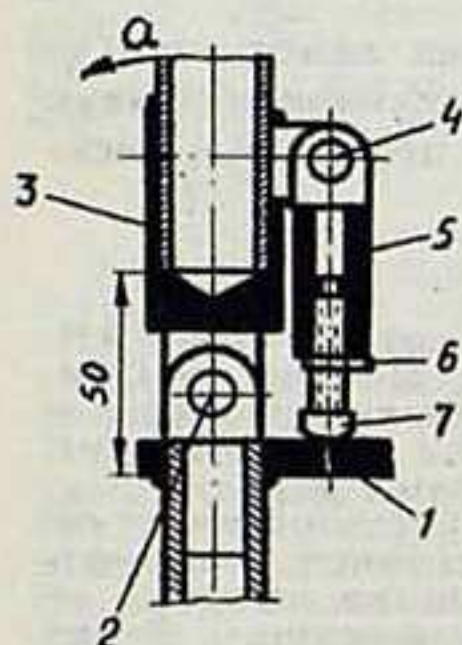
Механизм поворота спинки: 1 — основание; 2 — ось поворота; 3 — кронштейн; 4 — ось поворота упора; 5 — откидной упор; 6 — гайка; 7 — упорный винт.
